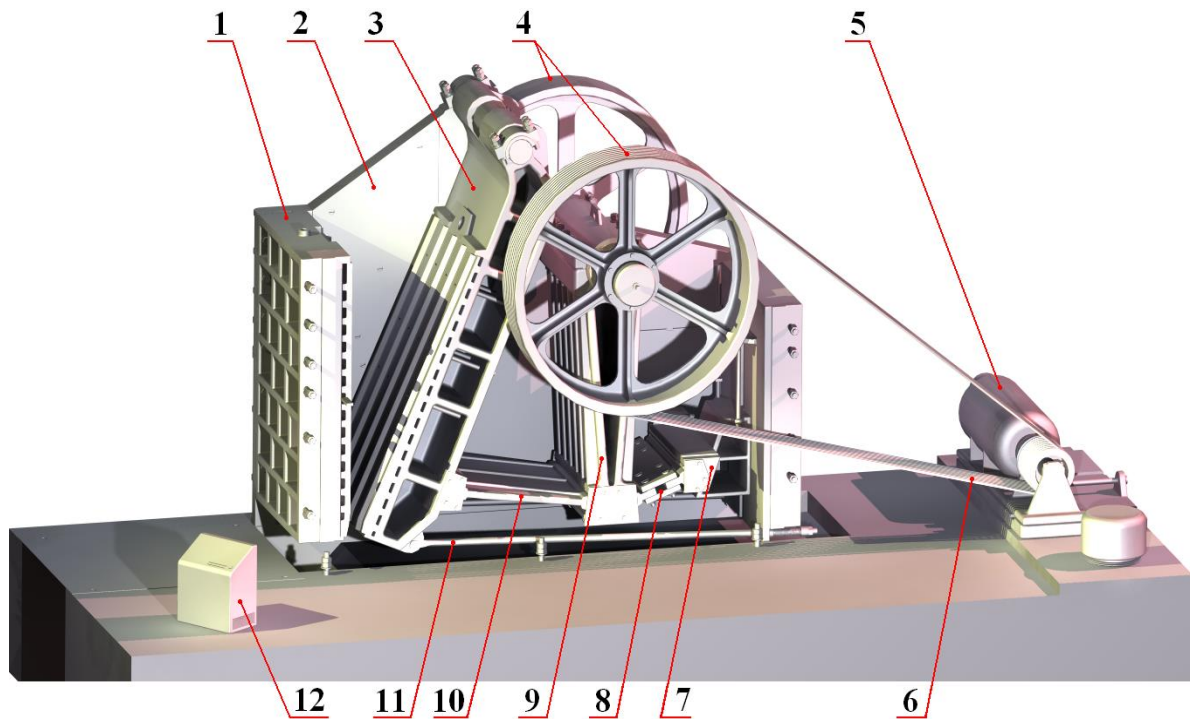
Зовнішній вигляд щоквої дробарки з простим рухом щоки
